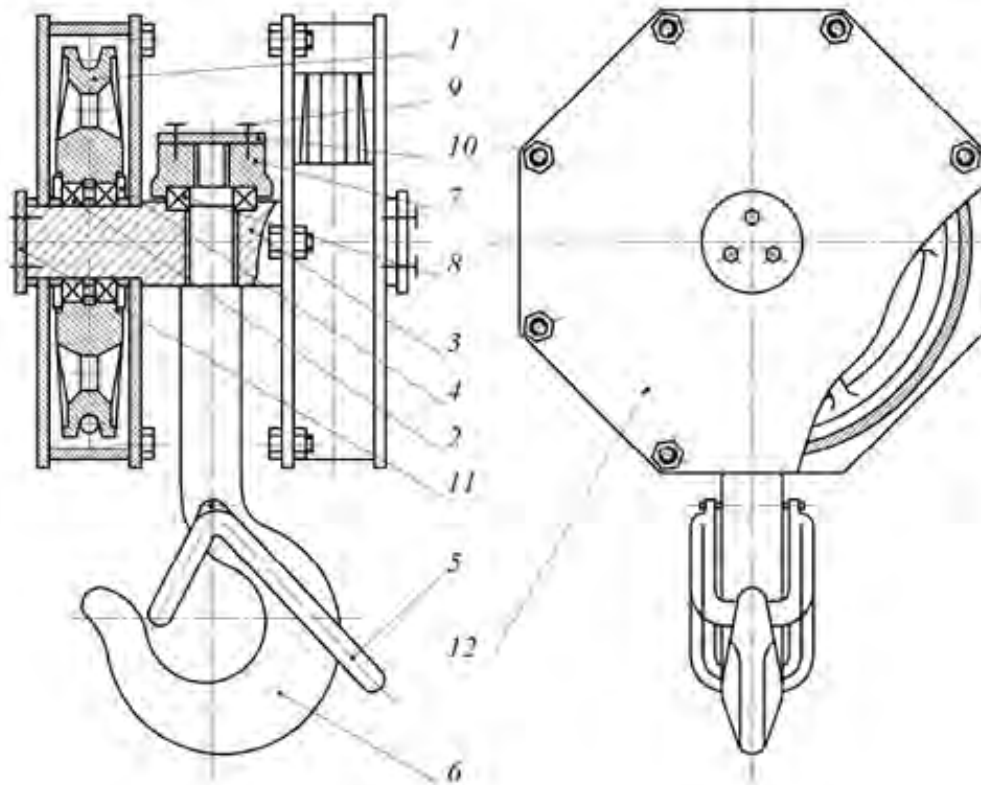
Укороченная подвеска: 1 – блок; 2 – радиальный подшипник; 3 – поперечина; 4 – крышка подшипника; 5 – замок; 6 – крюк; 7 – гайка; 8 – упорный подшипник; 9 – винт; 10 – торцевая шайба; 11 – стопорная шайба; 12 – защитный лист
